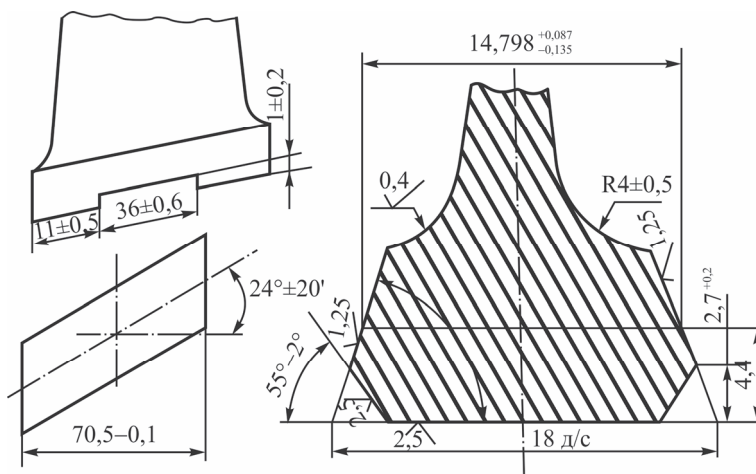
Эскиз замка лопатки компрессора двигателя ПС90 2А из титанового сплава ВТ8, обрабатываемого протягиванием
